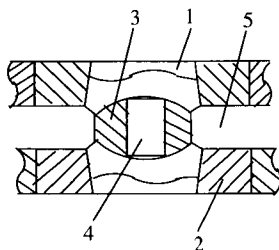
Схема камеры высокого давления с поддерживающими кольцами (наковальня с лункой):
